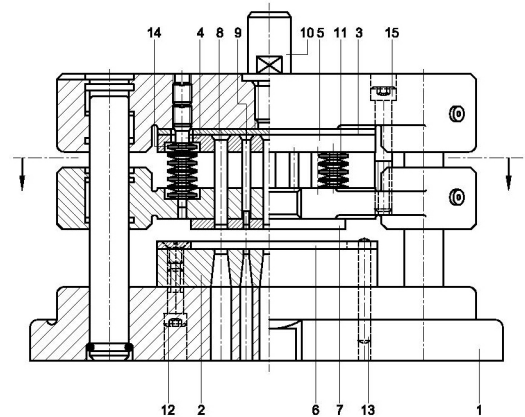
Säulenführungsschnitt mit Mehrfachloch
